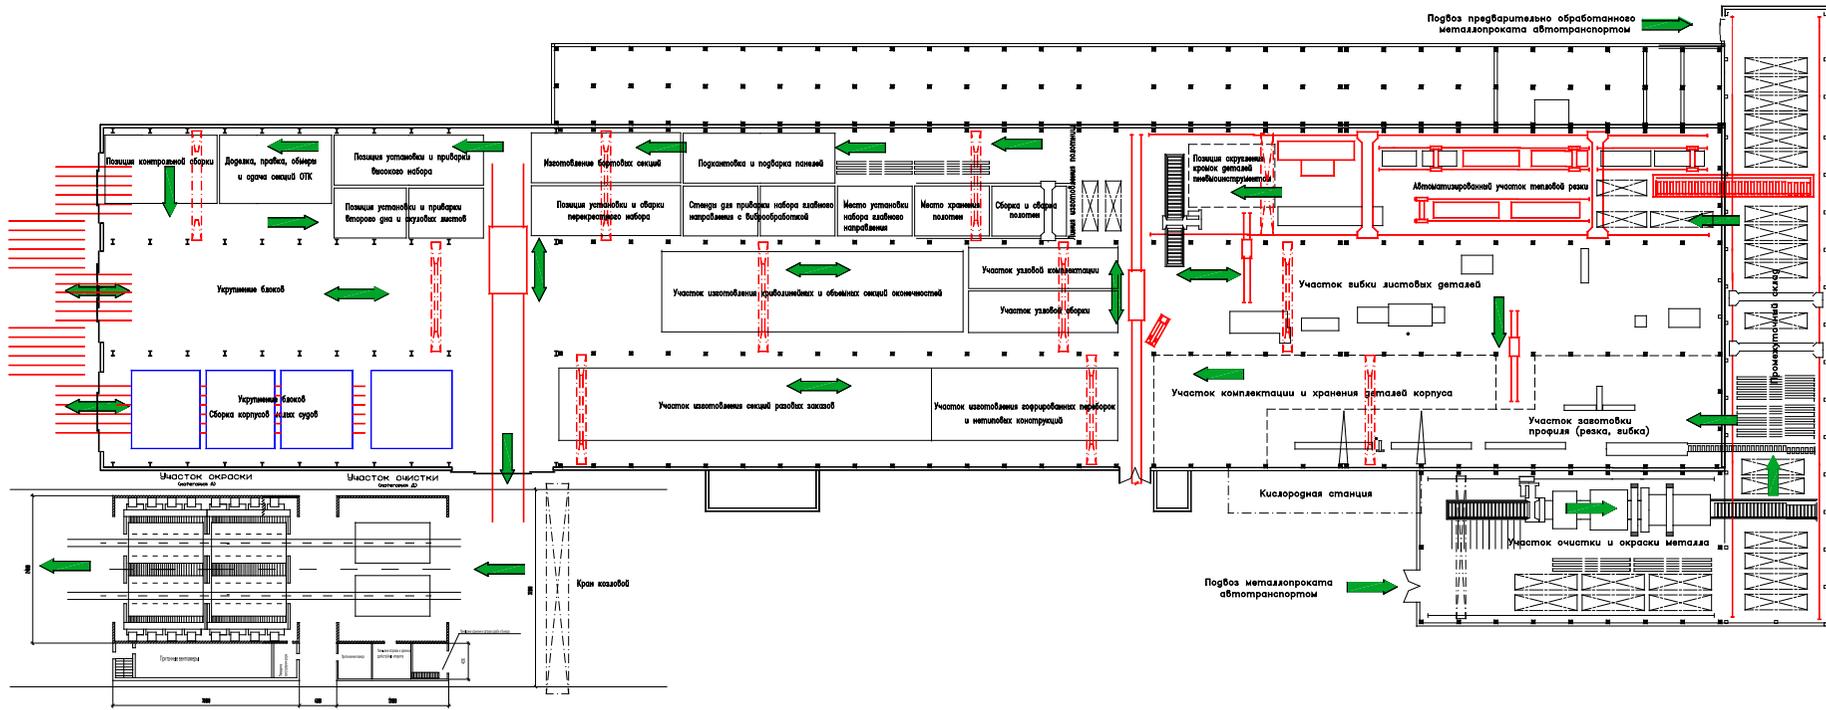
Схема металлопотоков блока корпусообработывающего и сборочно-сварочного производств
